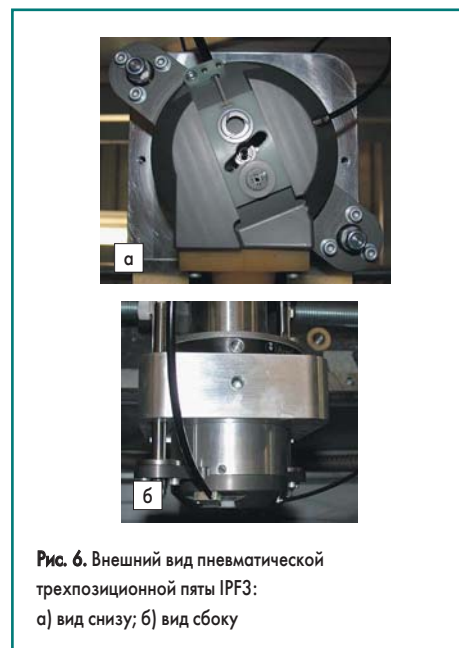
Внешний вид пневматической трехпозиционной пята IPF3:
